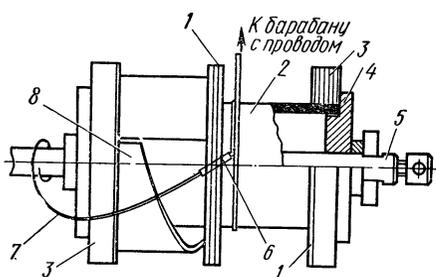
Намотка многослойной цилиндрической катушечной обмотки ВН трансформатора типа НОМ-35-66:
